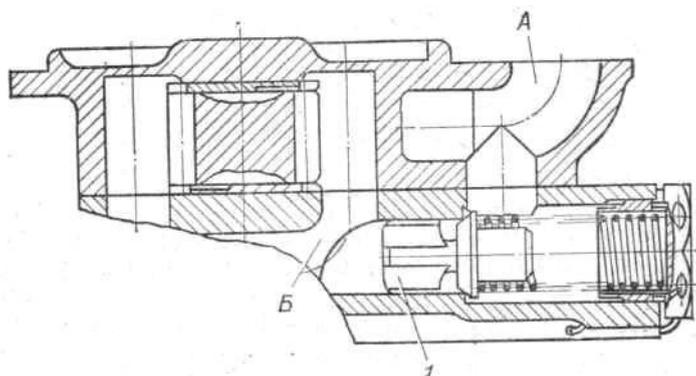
Откачивающий насос с обратным клапаном: А — полость всасывания; Б — полость нагнетания; 1 — обратный клапан
